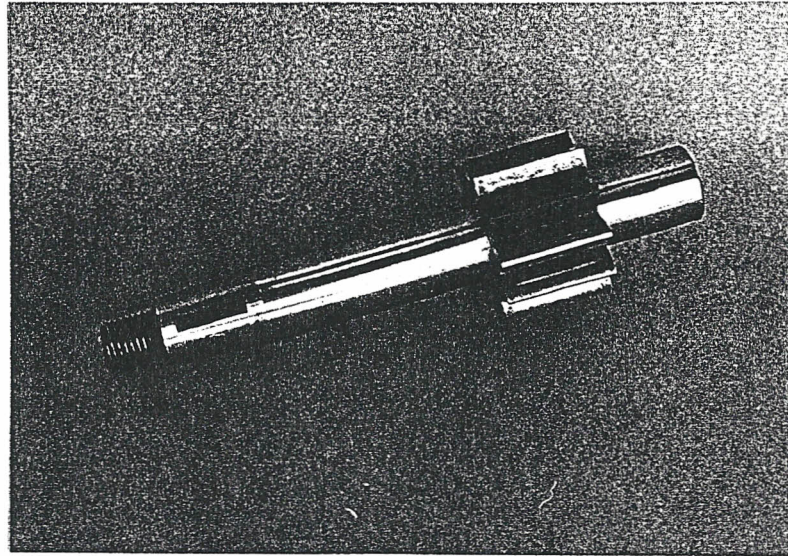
Ingranaggio conduttore della pompa di Fig. 2
